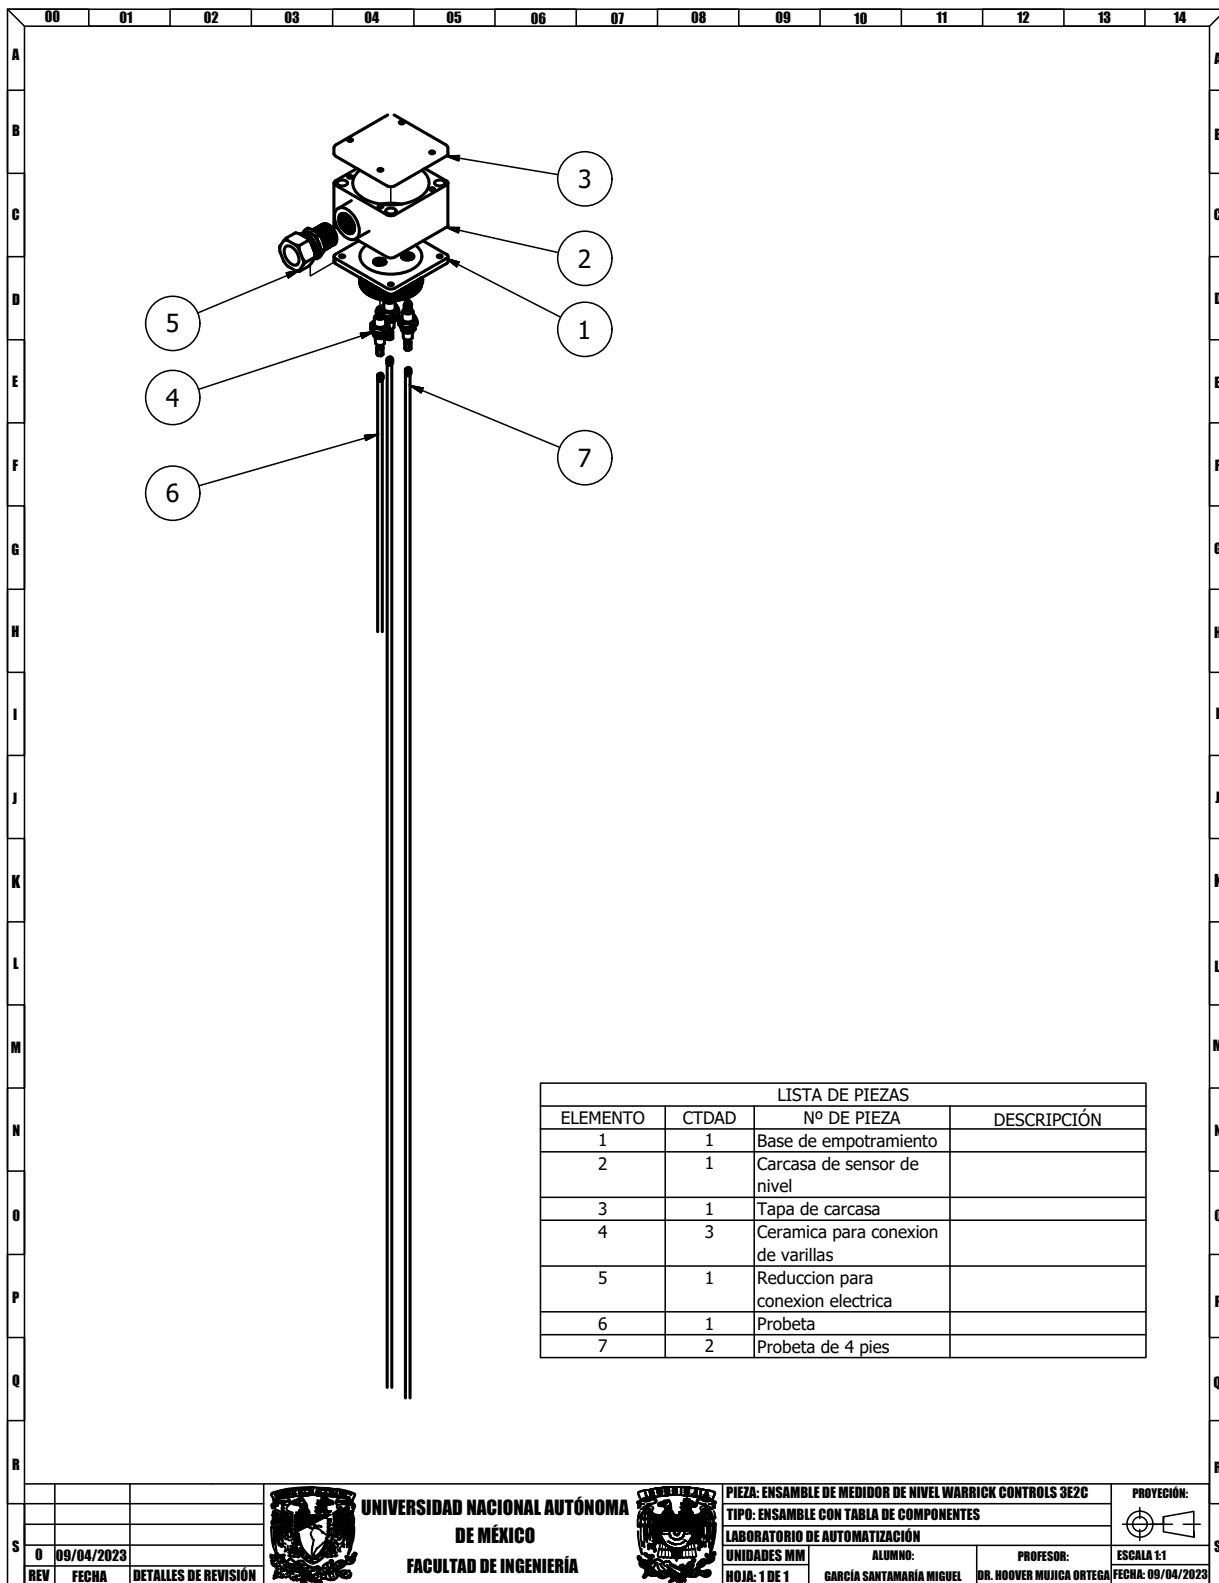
Ensamble explosionado y tabla de componentes de sensor de nivel Warrick
